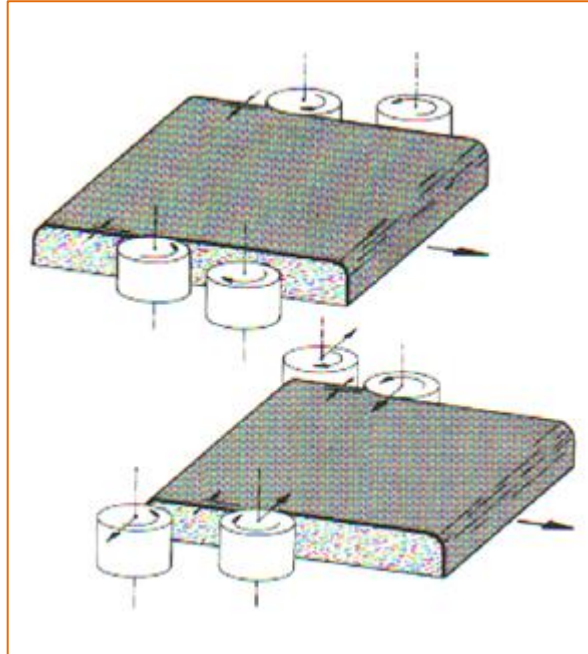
Schnittkantenbearbeitung mit einseitig gesteuerten Gleich- und Gegenlaufräsern
